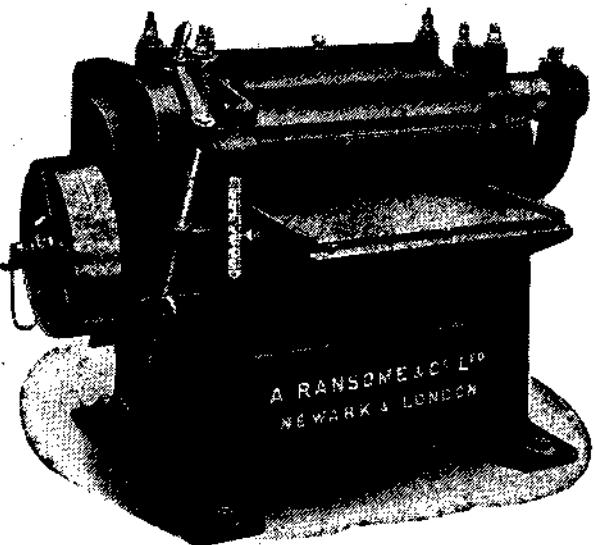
Вальцевый строгальный станок с одним ножевым валом.
